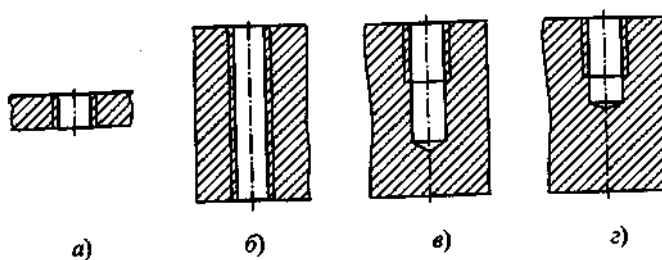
Типы отверстий для нарезания резьбы метчиками:
